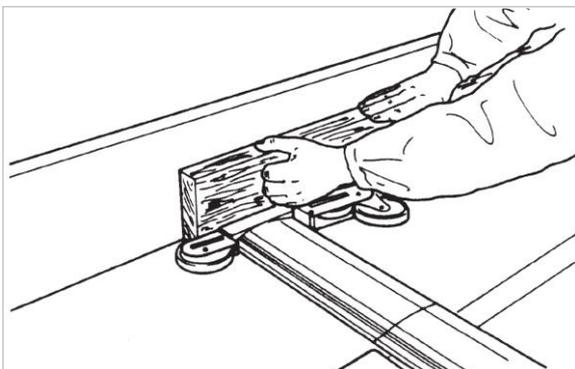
rabotage des bords de pièces de hauteur < 75 mm
